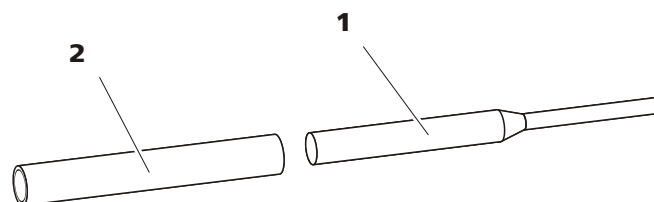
Werkzeug für Kolbendichtung (6.2617.010)
